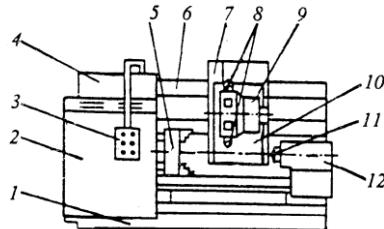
Схема токарного станка с ЧПУ: 1 – станина; 2 – передняя бабка; 3 – управляющий пульт; 4 – шкаф для управляющей аппаратуры с ЧПУ; 5 – приспособление для закрепления заготовки; 6 – направляющие; 7 – суппорт; 8 – инструмент; 9 – резцовая головка; 10 – салазки суппорта; 11 – центр; 12 – задняя бабка
